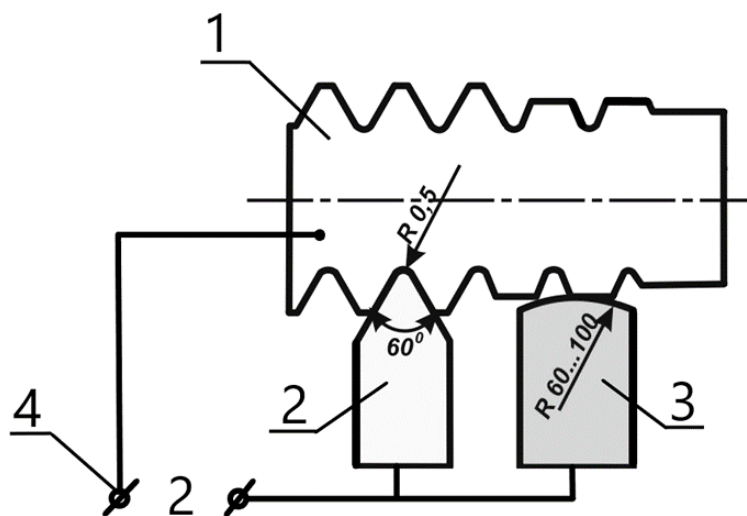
Схема восстановления поверхности детали применением электромеханической высадки и сглаживания: 1 – ось валка, 2 – высаживающий инструмент, 3- сглаживающий инструмент, 4 – источник питания.
